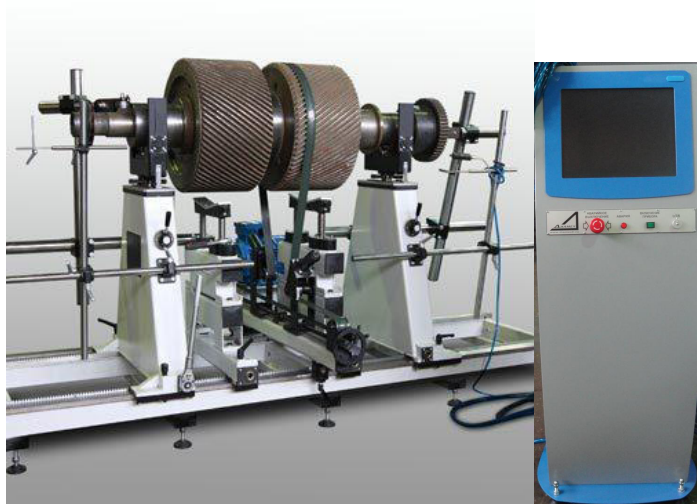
Общий вид станка балансировочного виброизмерительного ВМВ 3000
